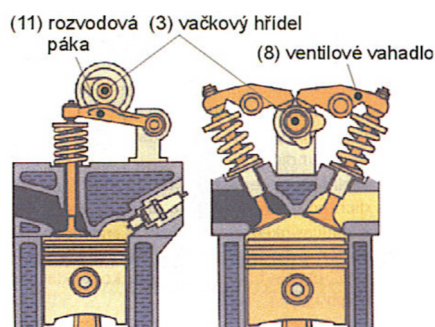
Rozvod OHV (Over Head Valves) [3].
